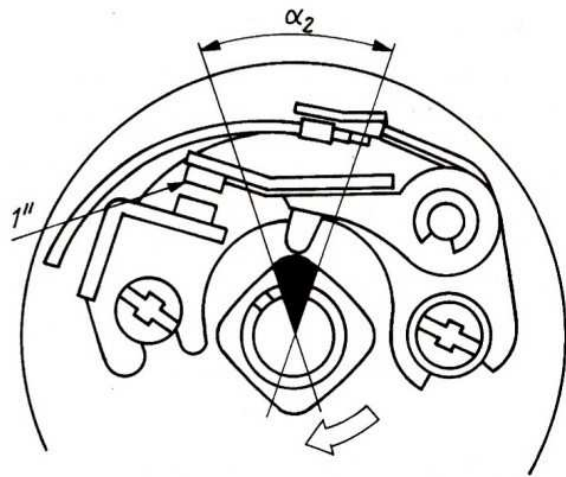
Podzespół przerywacza aparatu zapłonowego:
